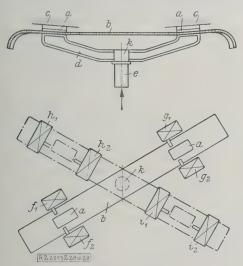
und 31 Vorrichtung der Firma Fried. Krupp A.-G. zum gleichzeitigen Aufschweißen mehrerer Platten auf eine Unterlage.
